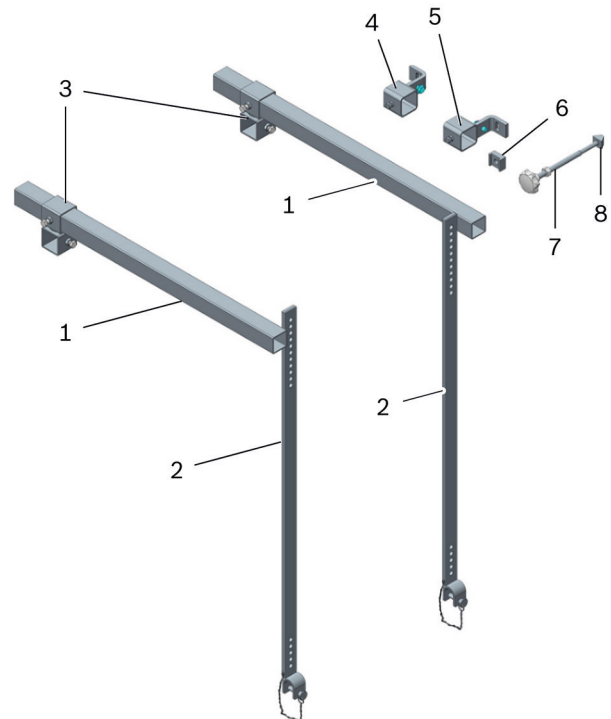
Стандартный комплект опорного приспособления для двигателя T40091
